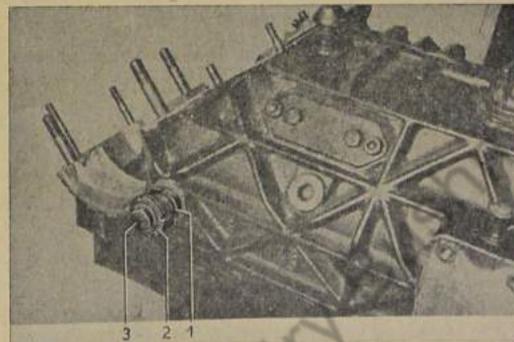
Einstellschraube für Tellerrad-abstützung einschrauben
